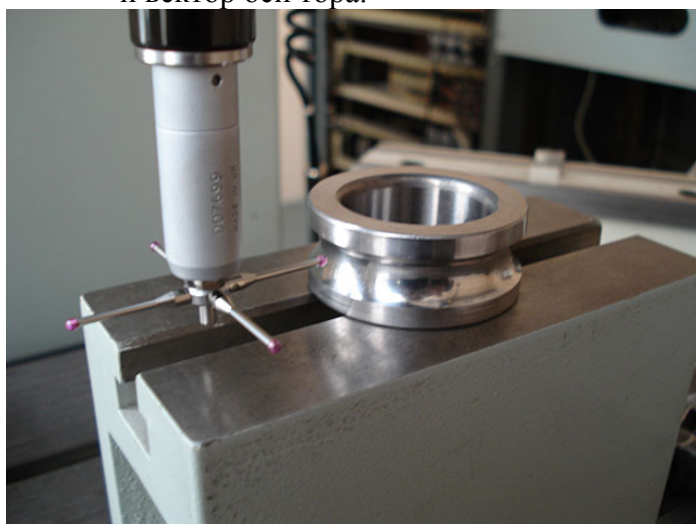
Измерение беговой дорожки кольца шарикового подшипника
